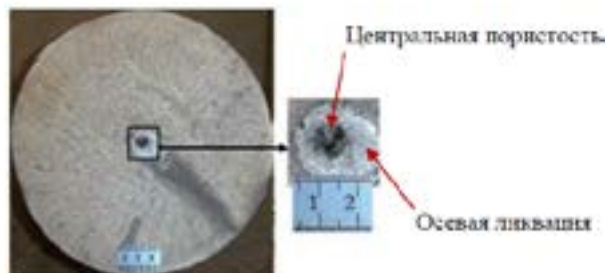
Центральная пористость и осевая ликвация трубной непрерывнолитой заготовки
